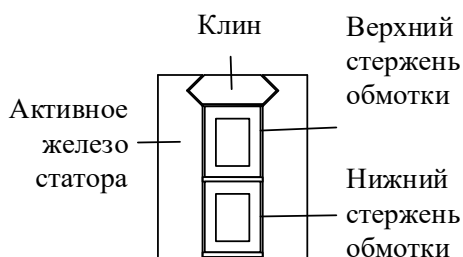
Схематическое изображение расположения клина в пазовой части обмотки статора
